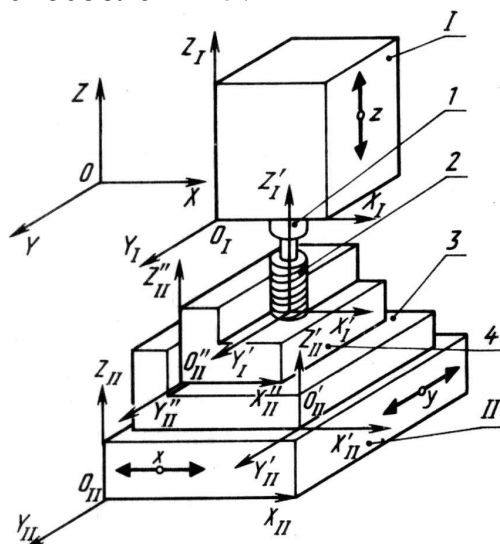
Схема обработки заготовки на многоцелевом станке с ЧПУ вертикальной компоновки
